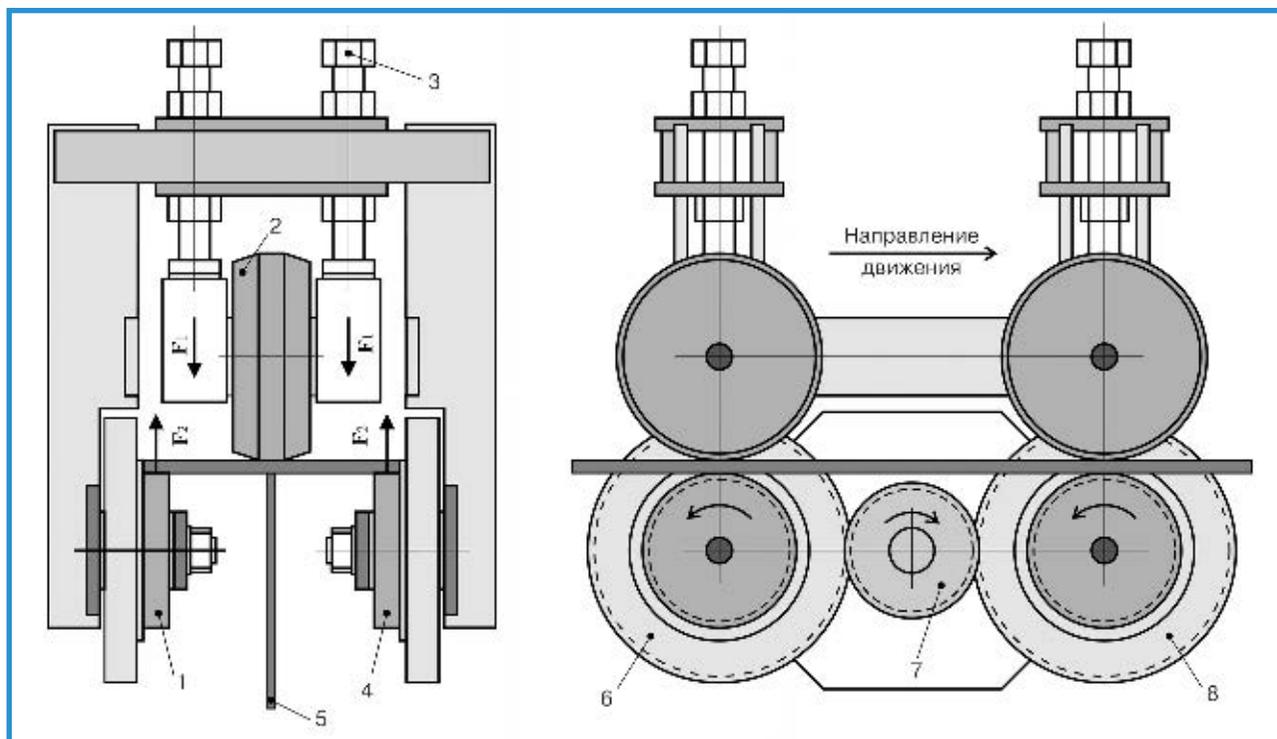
Принцип работы устройства для правки двутаврового профиля (мотор-редуктор не показан)
